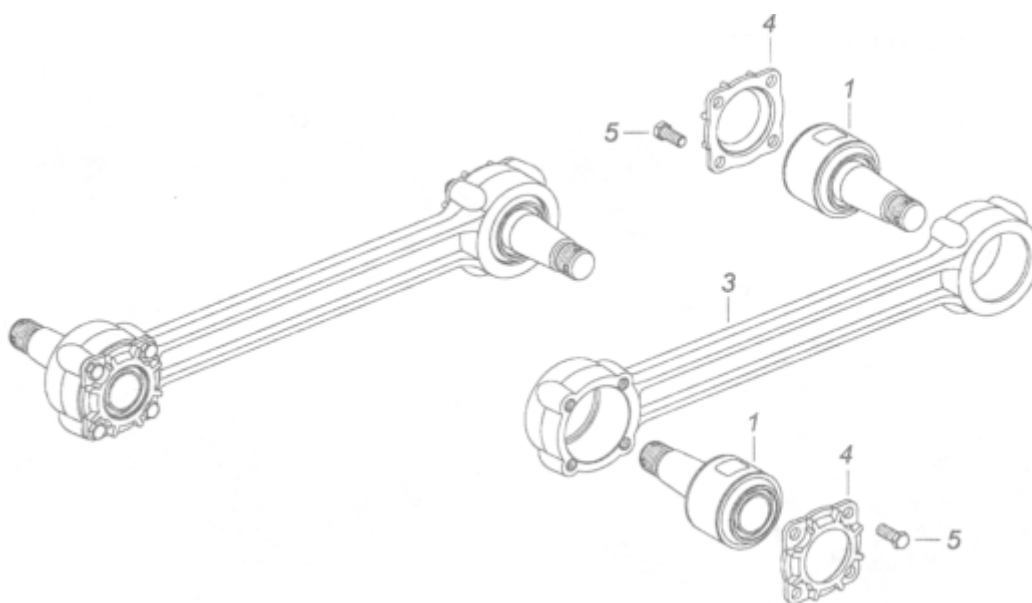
Реактивная штанга: 1 - шарнир реактивной штанги; 3 - штанга реактивная; 4 - крышка реактивной штанги; 5 - болт.
